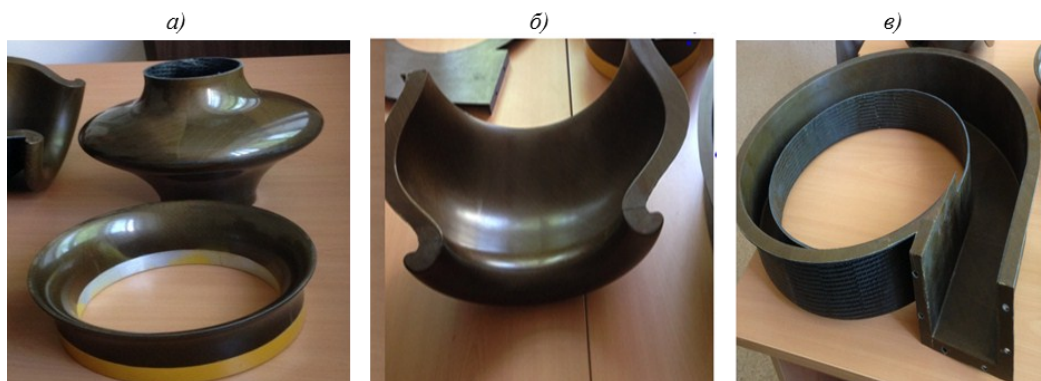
Элементы ПЗУ, изготовленные из углепластика ВКУ-42 с лакирующим слоем органоупластика: а – разделитель и верхняя стенка корпуса; б – верхняя стенка; в – верхняя часть «улитки» ПЗУ
